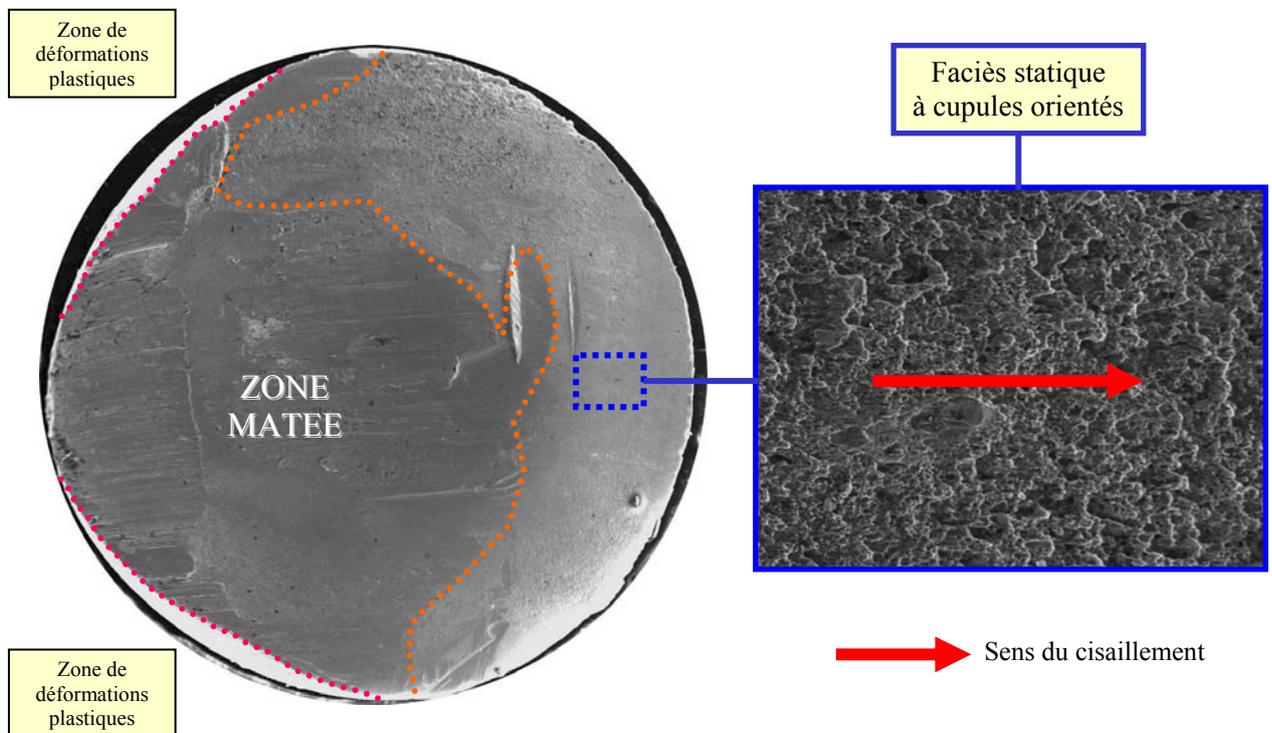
faciès de rupture du pion de guidage situé sur l'entretoise de blocage
